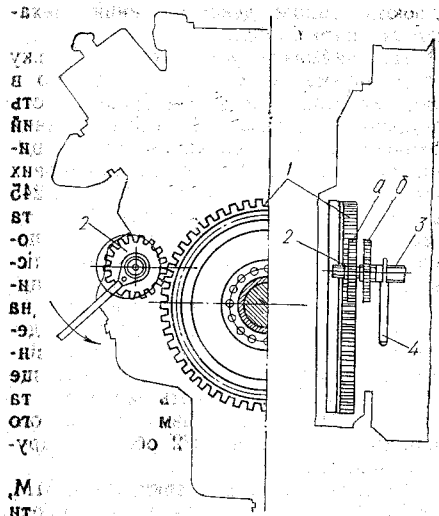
Механізм повороту колінчастого вала двигуна ЯМЗ-2405:
